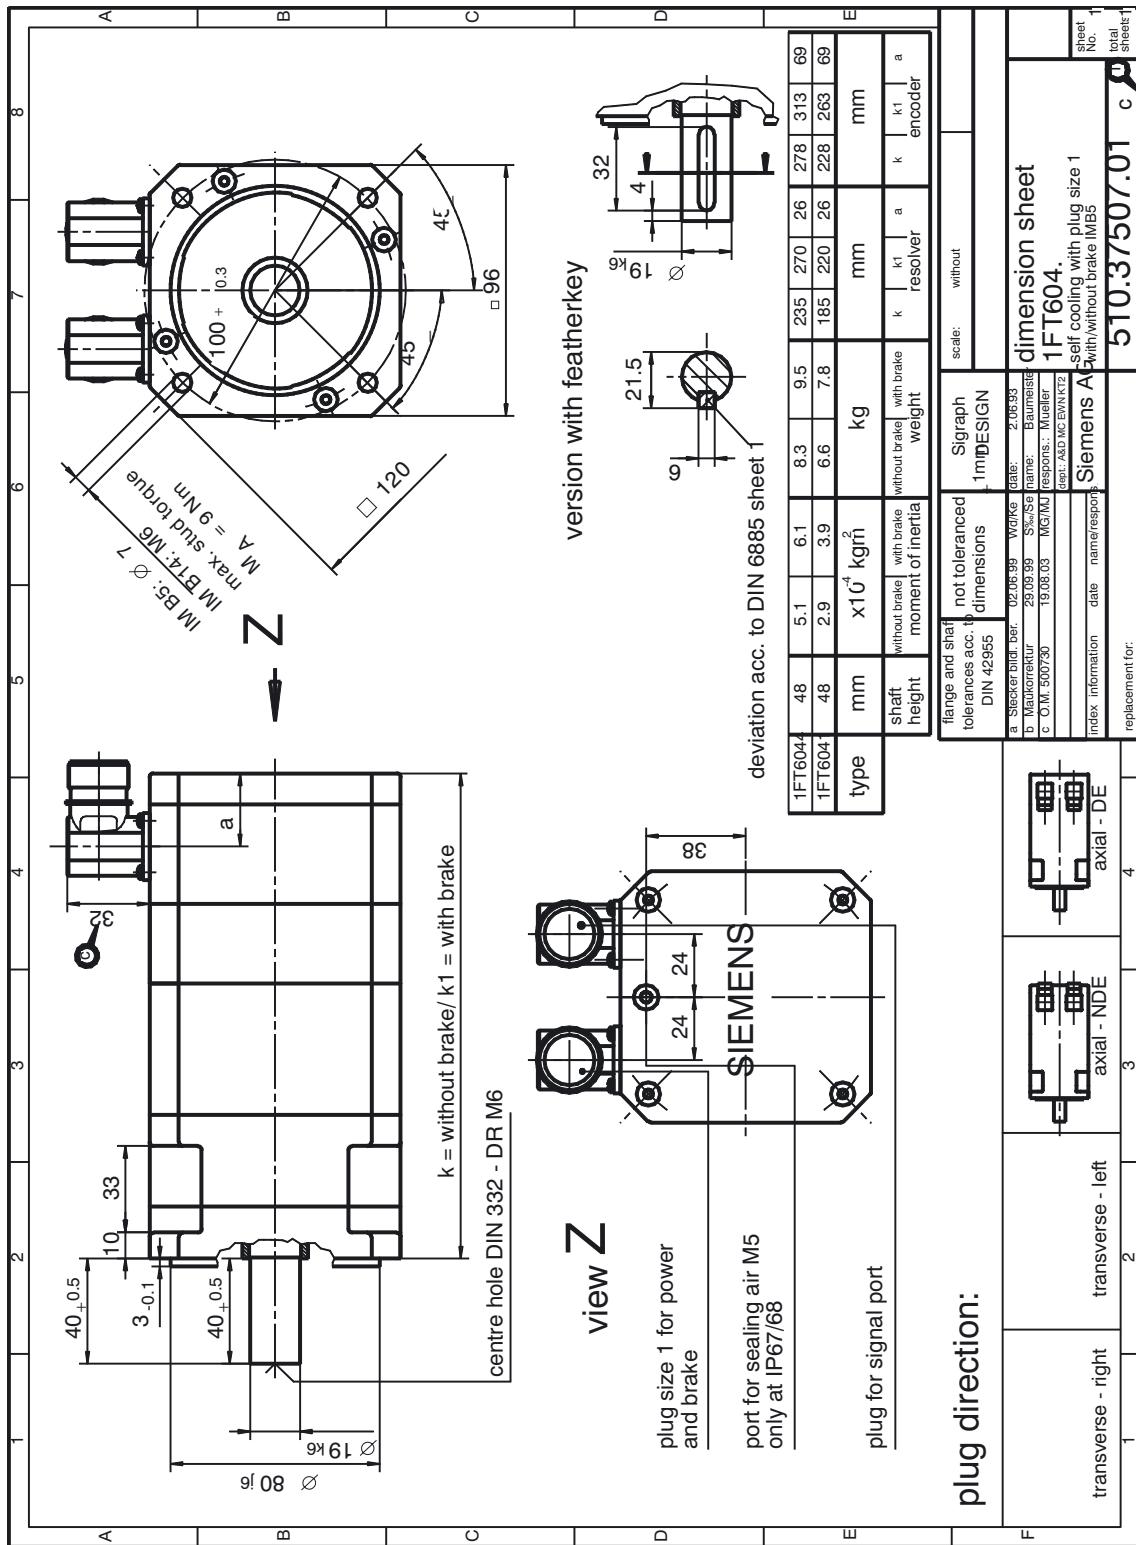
1FT604□ selbstgekühlt mit Stecker Größe 1
